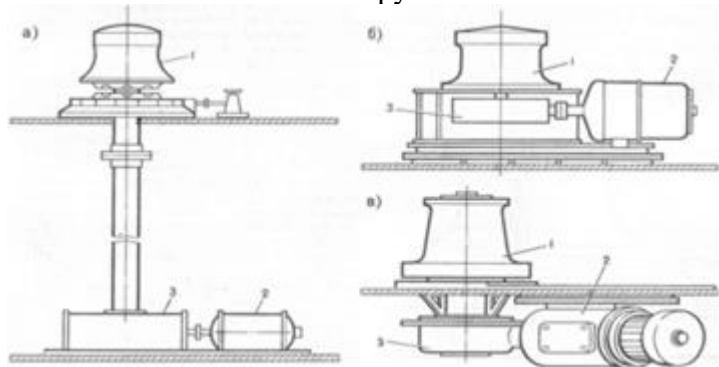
Схемы расположения шпильей: а) двухпалубное; б) надпалубное; в) подпалубное; 1-турачка; 2-электродвигатель; 3-редуктор
